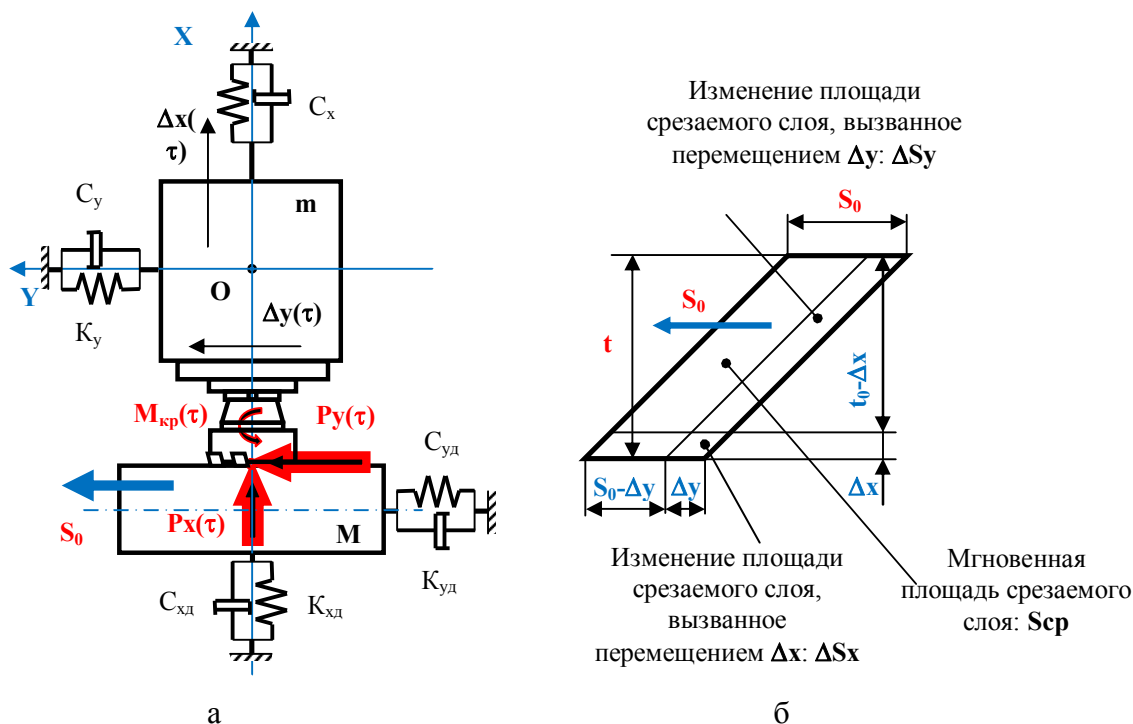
Расчетная схема эквивалентной упругой системы тяжелого фрезерного станка: а – расчетная схема технологической системы тяжёлого фрезерного станка; б – схема площади среза при фрезеровании торцевой фрезой
